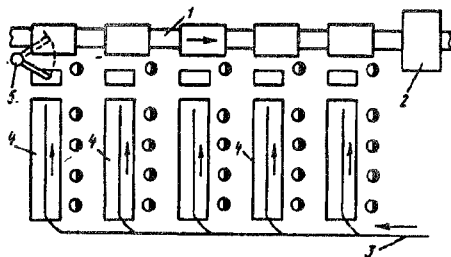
Схема потоков узловой и общей сборки: 1 — поток общей сборки; 2 — камера окраски и сушки; 3 — грузопоток деталей; 4 — линии узловой сборки; 5 — кран-укосина
